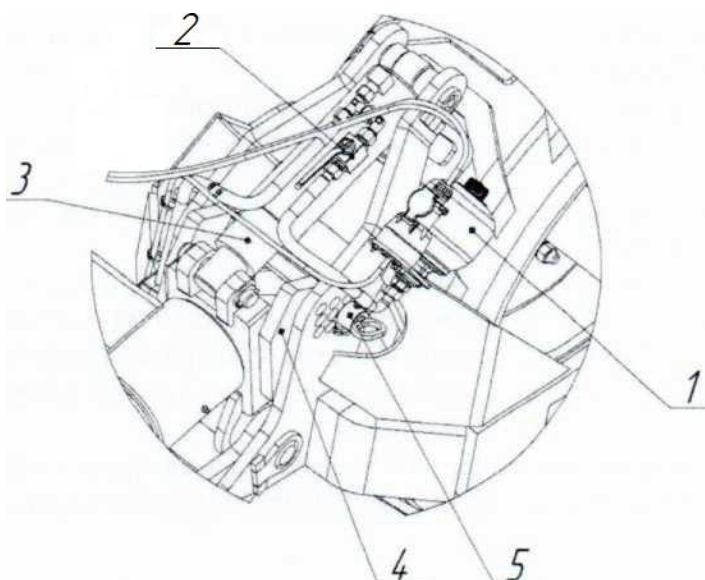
Перевод гидроцилиндра опорного колеса в транспортное положение
